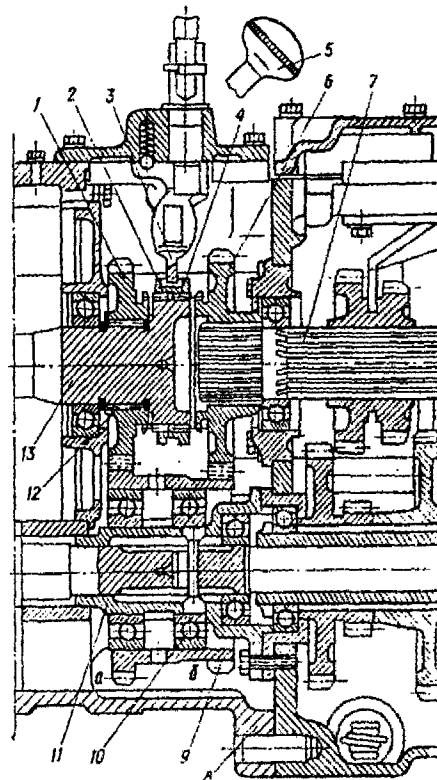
Понижающий редуктор коробки передач тракторов семейства МТЗ: 1 – ведущая шестерня редуктора; 2 – зубчатая муфта; 3 – вилка; 4 – зубчатый венец вала сцепления; 5 – рычаг управления редуктором; 6 – ведомая шестерня редуктора; 7 – первичный вал коробки передач; 8 – корпус сцепления; 9 – блок шестерен; 10 – шариковый подшипник; 11 – кронштейн; 12 – игольчатый подшипник; 13 – вал сцепления
